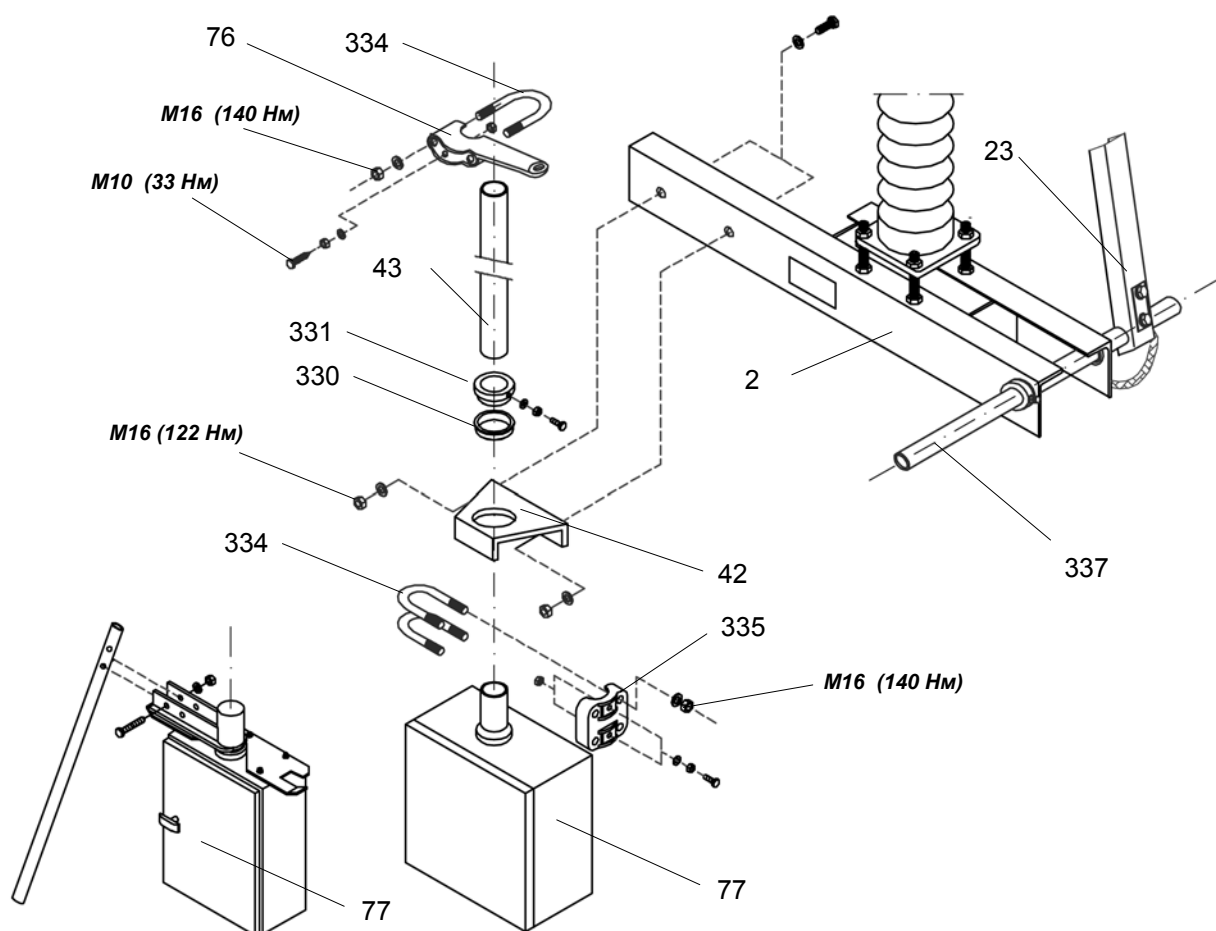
Крепление привода заземлителя – опосредованный монтаж
